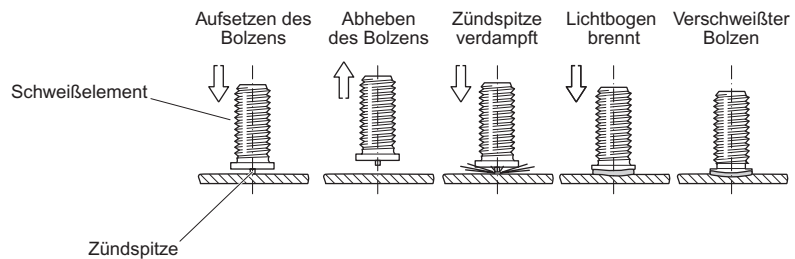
4 Abfolge beim Spalt-Bolzenschweißverfahren
